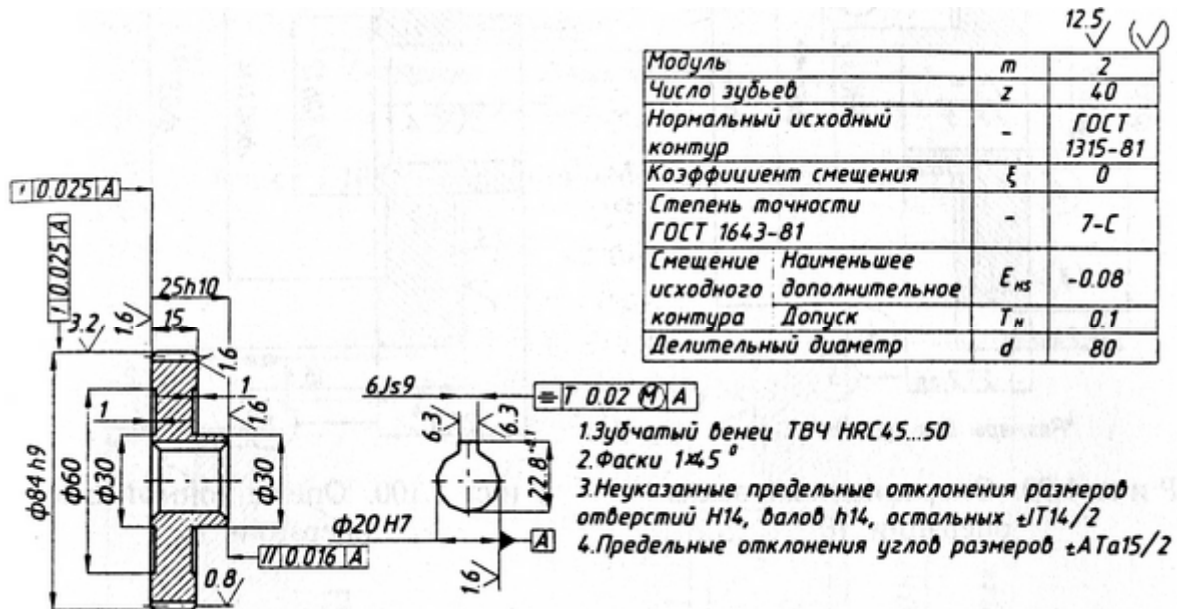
Цилиндрическое зубчатое колесо со ступицей
